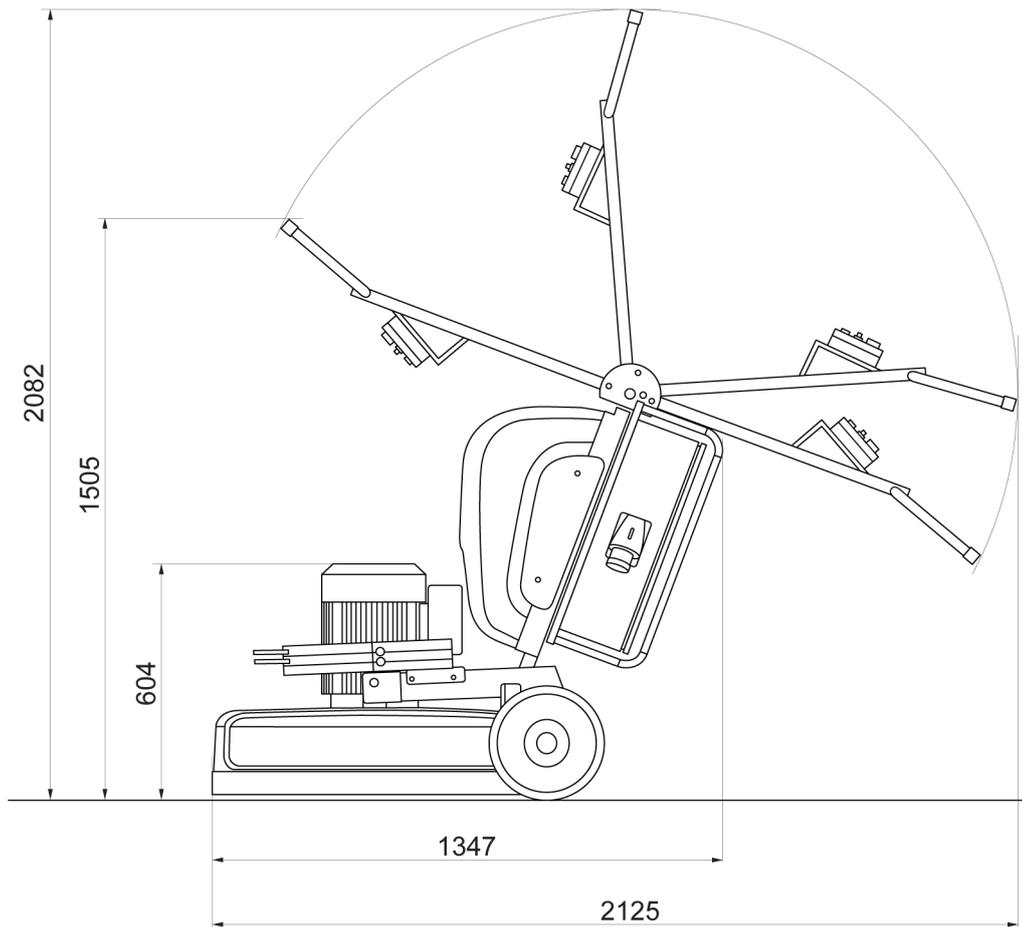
Höhen- und Längenmaße der Maschine in Millimeter
